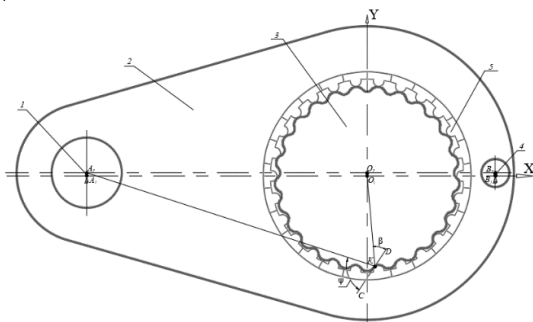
Схема зацепления колес эксцентриковой передачи с параллельным расположением входного и выходного валов
